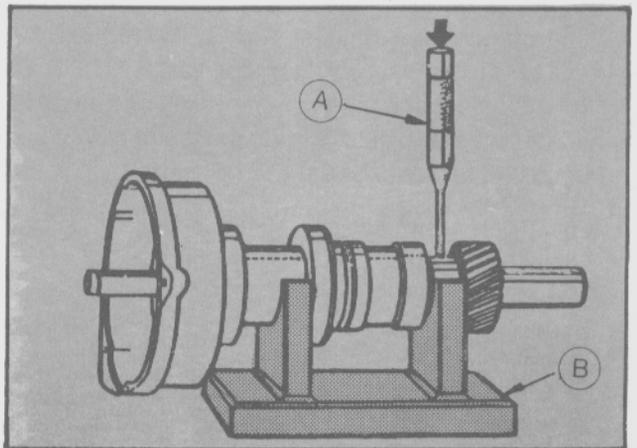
Desmontaje del perno de retención del engranaje conductor.
